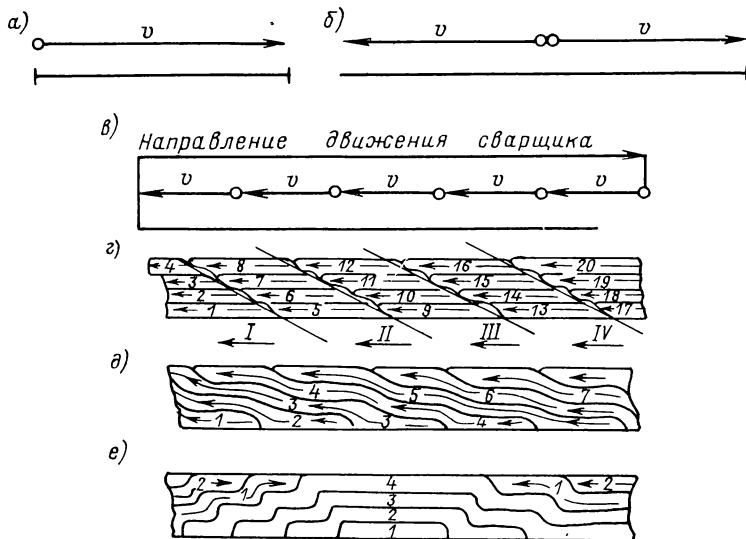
Приемы выполнения шва по длине: а — напроход; б — от середины к концам; в — обратноступенчатым методом; г — сварка блоками; д — сварка каскадом; е — сварка «горкой».
